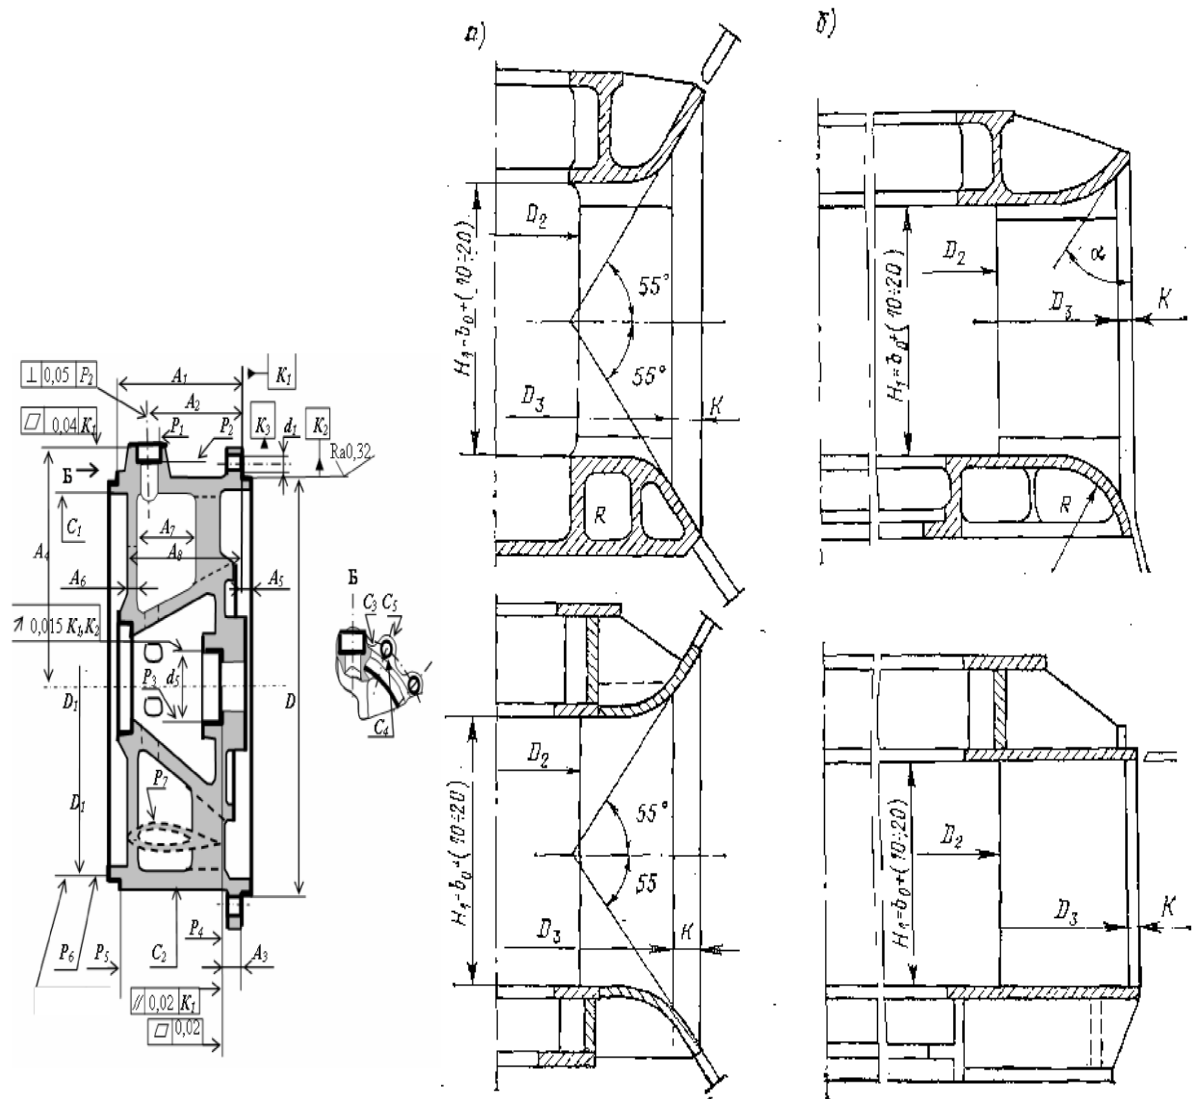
Корпусні деталі газотурбінних двигунів виготовлені ЛИТВОМ.
